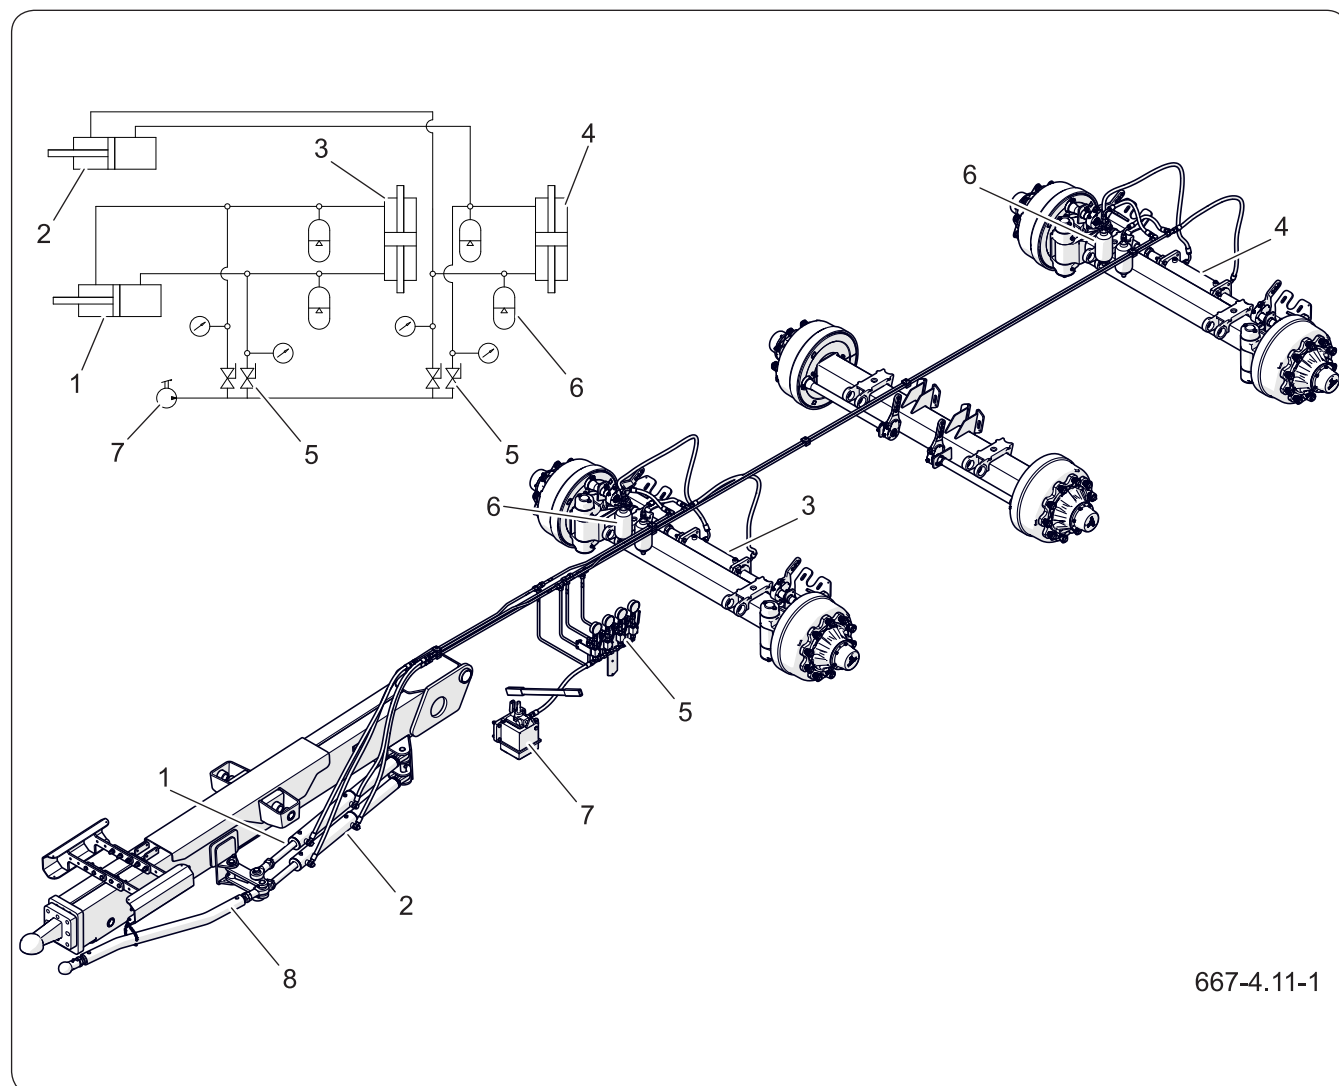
Konstrukce a schéma hydraulické instalace oje
